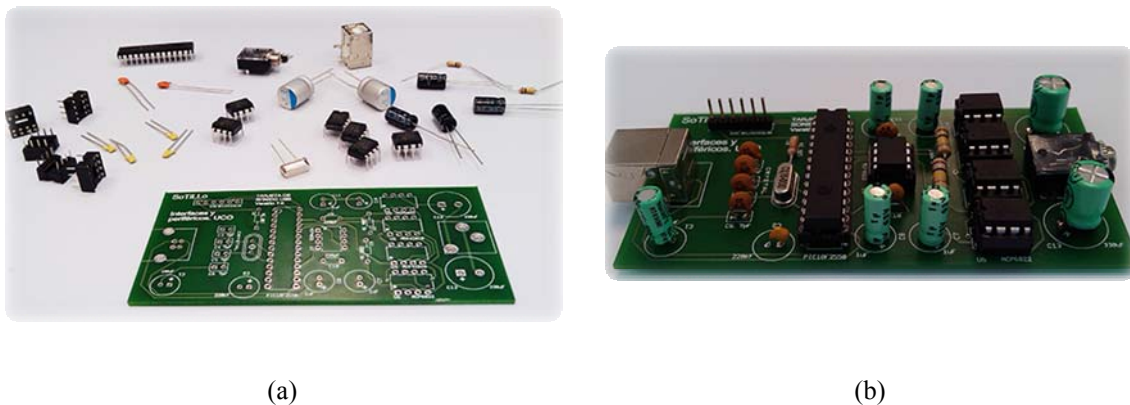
(a) Placa PCB y componentes electrónicos. (b) resultado final.
